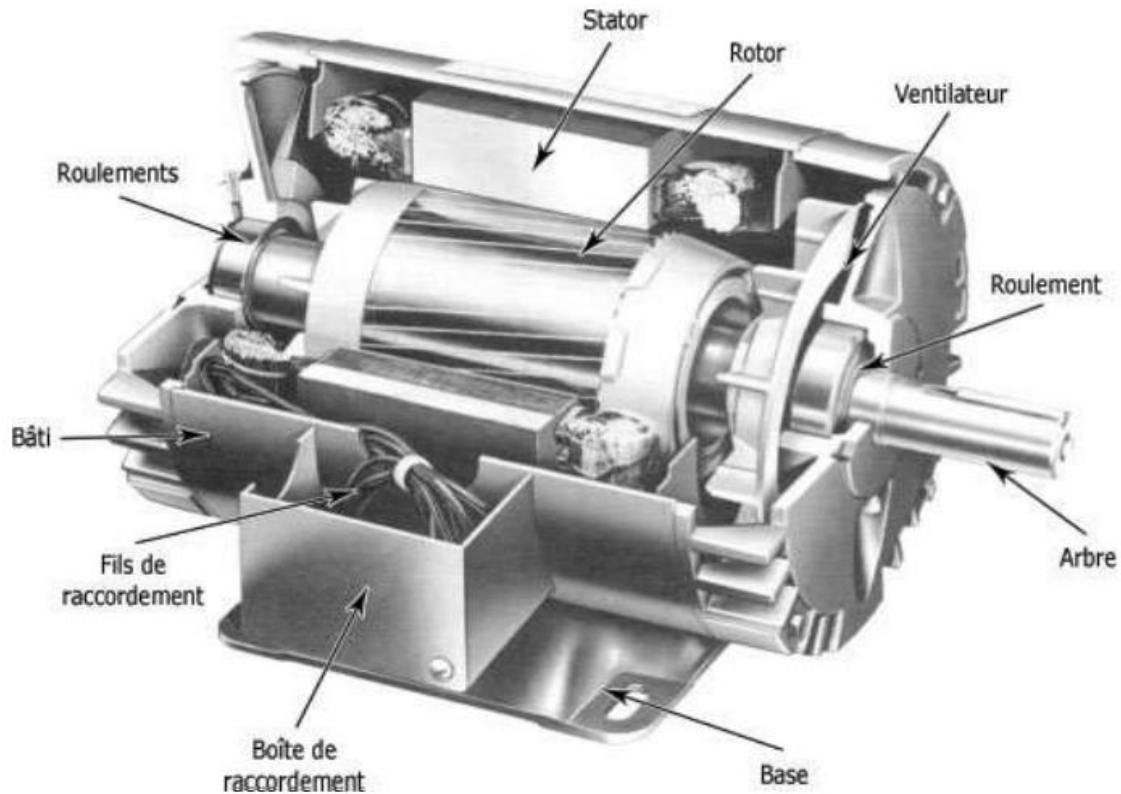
Éléments de constitution d'une machine asynchrone à cage d'écureuil
